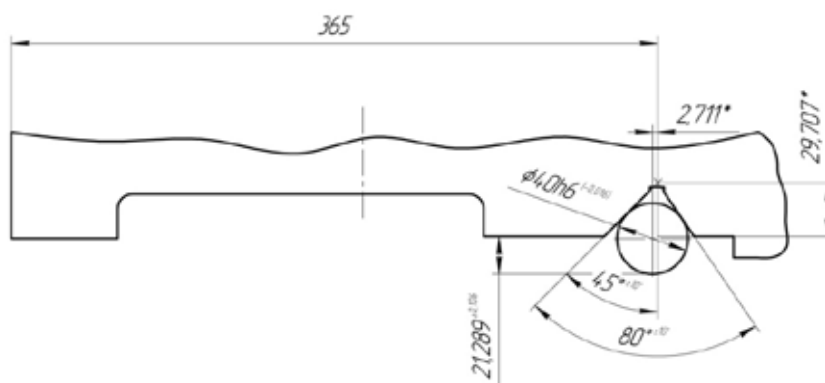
Шаблон для изготовления направляющих станины станка НТ-250И под суппорт
